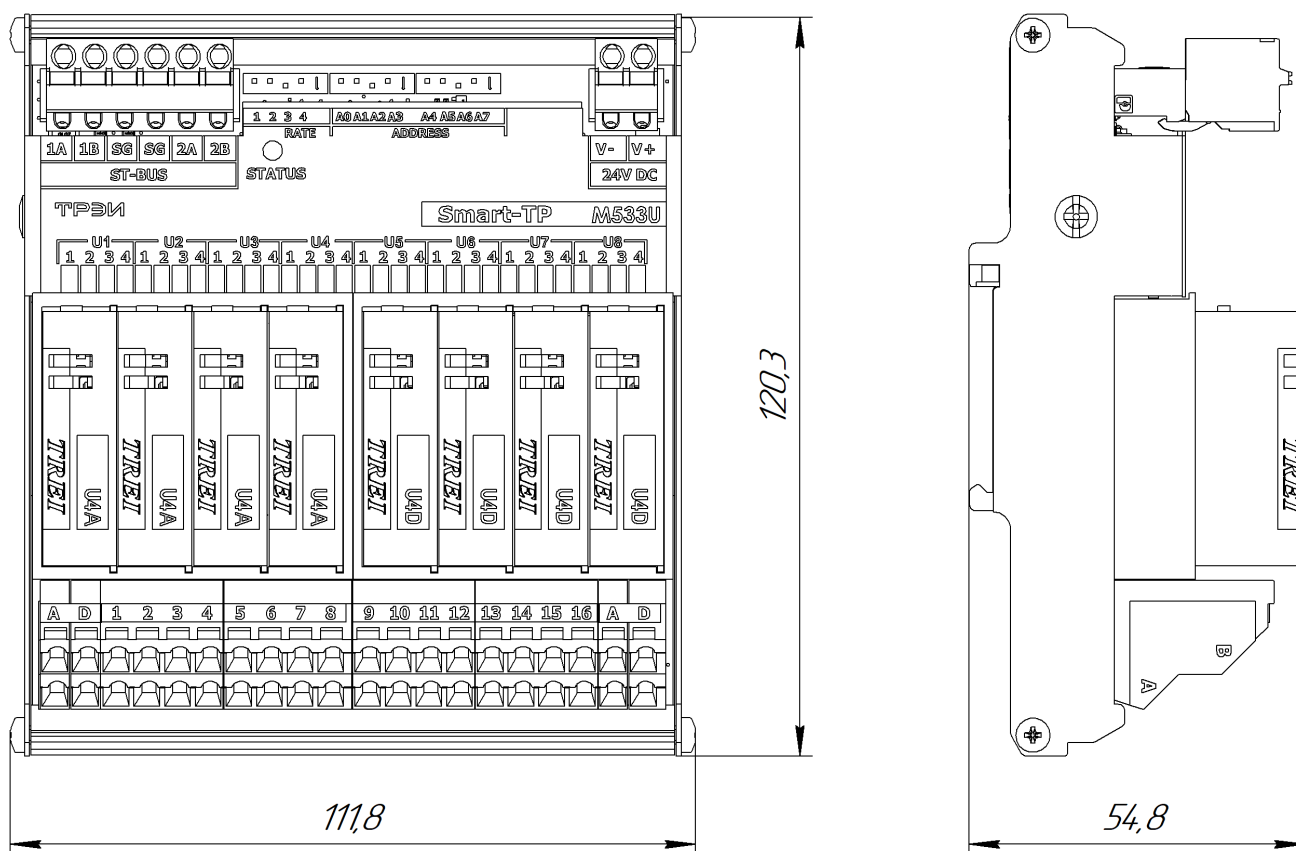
Чертеж общего вида M533U с указанием габаритных и присоединительных размеров
